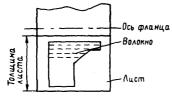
Схема вальцовки фланца приварного встык по плоскости листа
